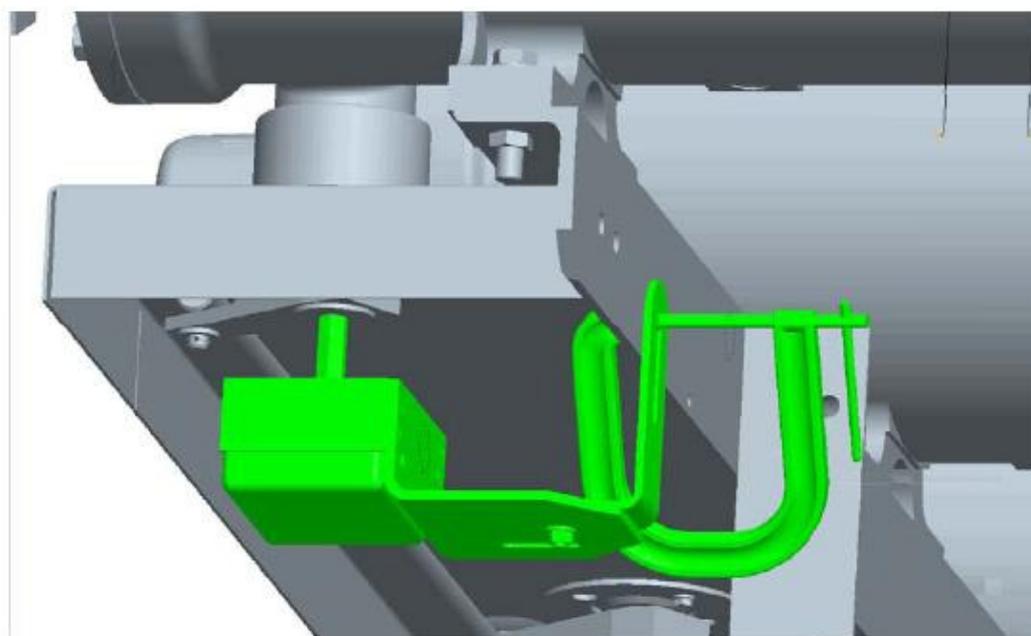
Montagem do Transdutor Rotativo Doble TR 3190
